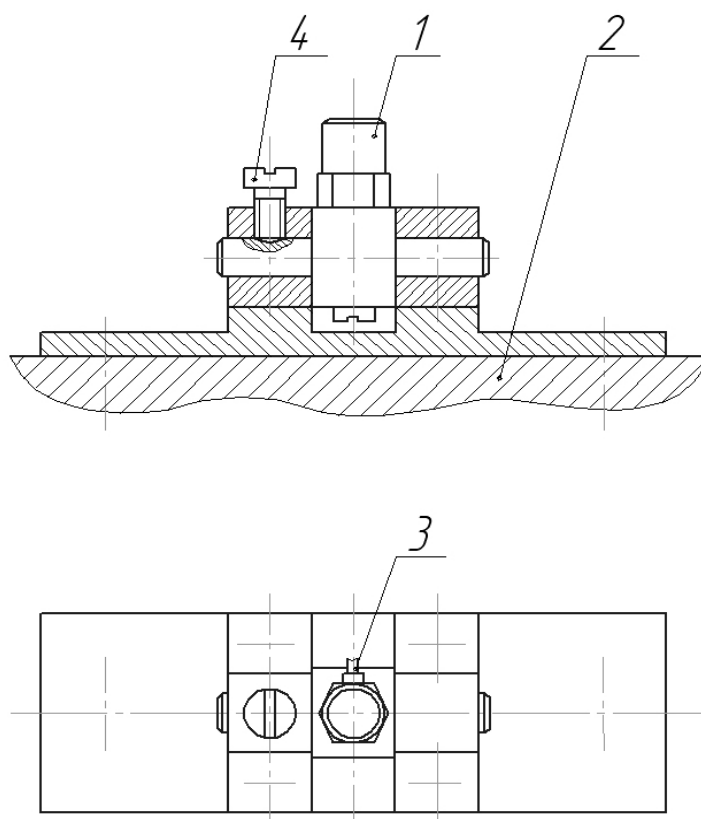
Переходное устройство для крепления вибропреобразователя к вибростолу:
